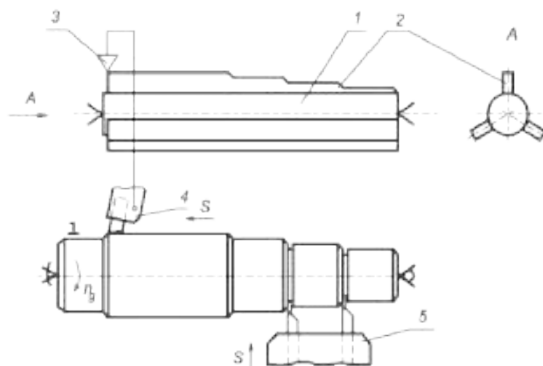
Схема обробки вала на копіювальному напівавтоматі: 1 — барабан; 2 — копів; 3 — щуп; 4 — повздовжній супорт; 5 — поперечний супорт
